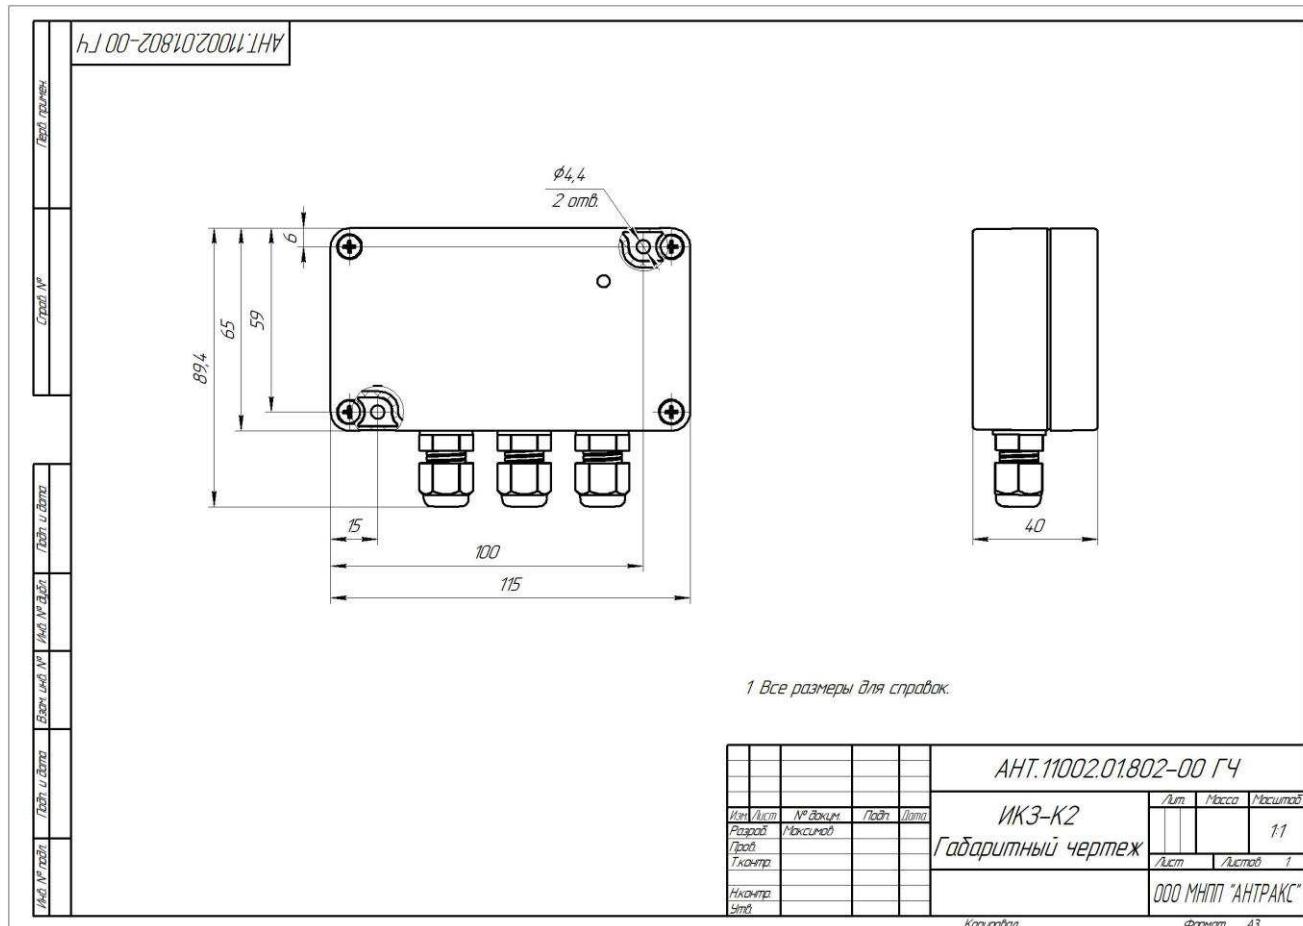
Габаритный чертеж индикатора ИКЗ-К2
